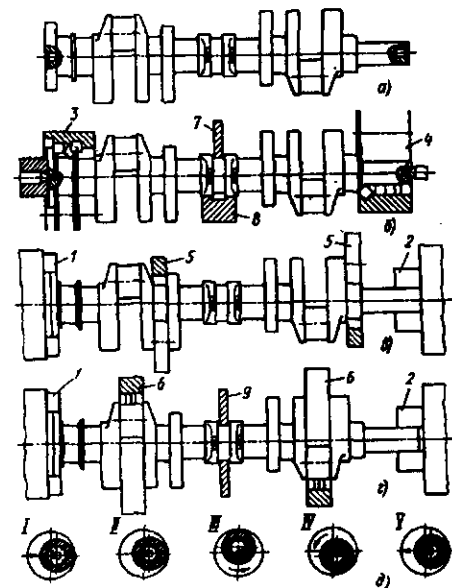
Схемы контурного фрезерования коленчатого вала: а – заготовка; б – фрезерование хвостовика и фланца; в – фрезерование коренных шеек; г – фрезерование шатунных шеек; д – положение фрезы в процессе обработки
